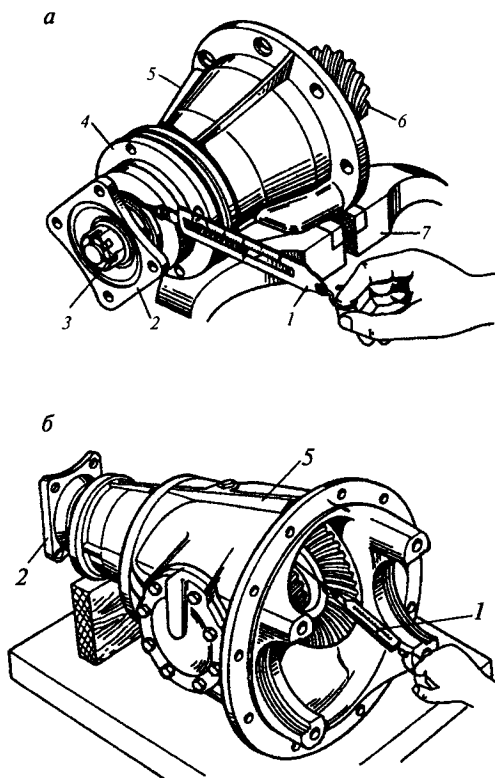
Проверка затяжки подшипников вала ведущих конической (а) и цилиндрической (б) шестерен:
